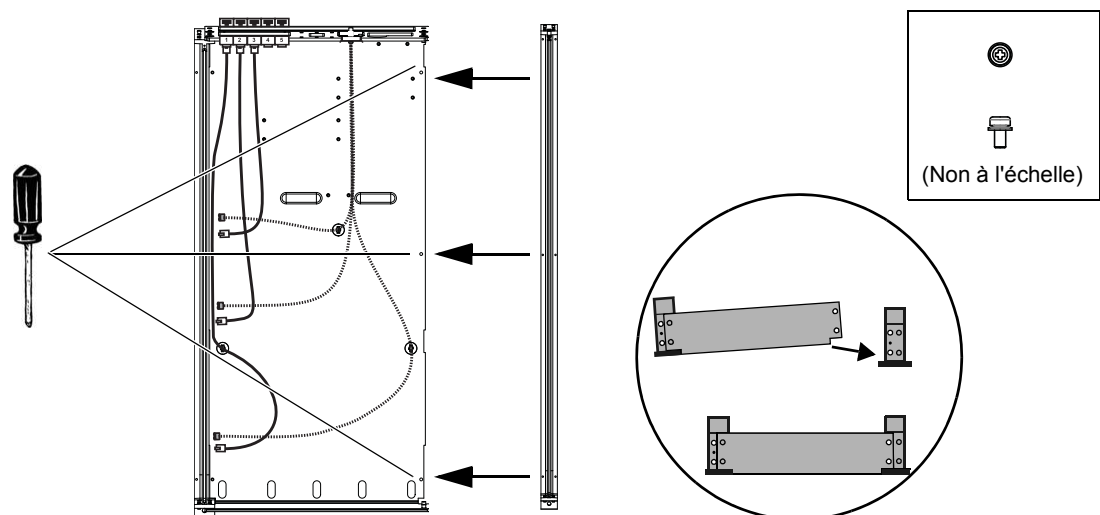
Fixation de la paroi extérieure sur la plaque de fond d'un bac, vue de dessus (à gauche) et de devant (en bas à droite)
